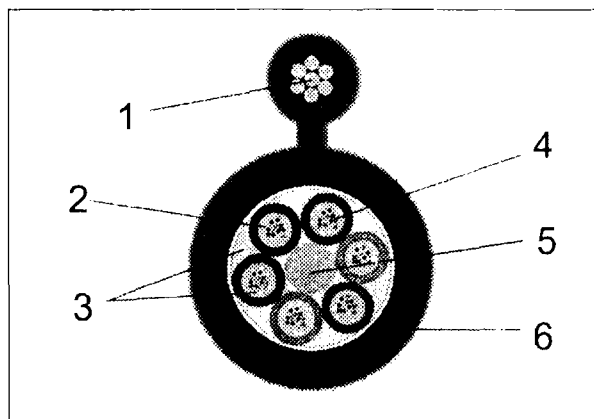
Поперечный разрез оптического кабеля для подвески с несущим силовым элементом марки ОПД
